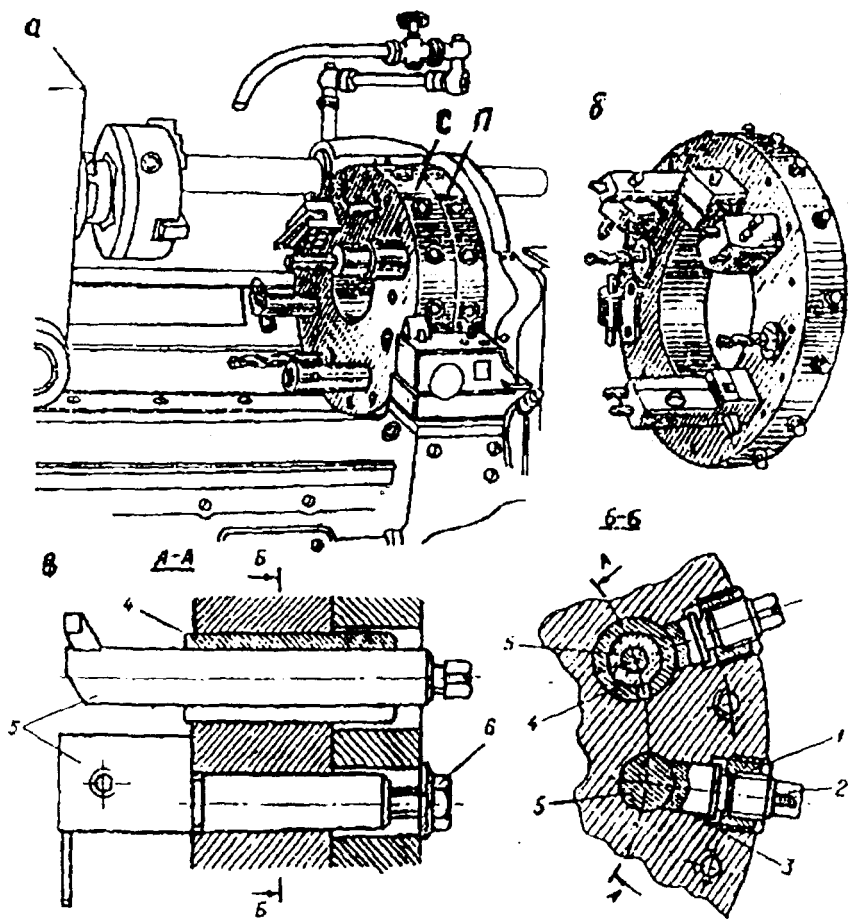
Наладка револьверного станка (а), настройка съемной части головки (б) и крепление державки в головке (в)
